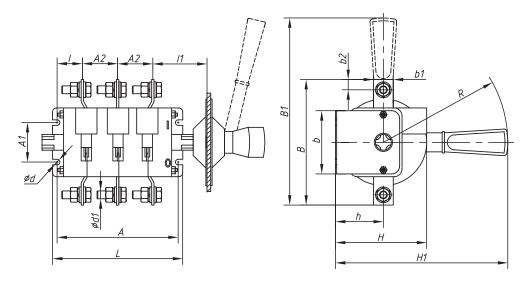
Выключатель-разъединитель универсальный трехполюсный на одно направление с д/г камерами, съемная левая/правая рукоятка
